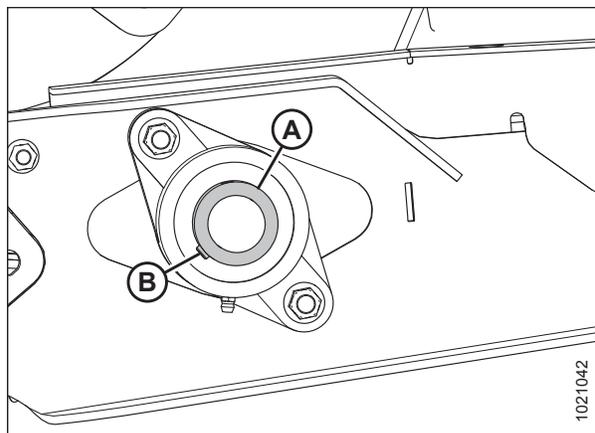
Подшипник приводного ролика подающего полотна
